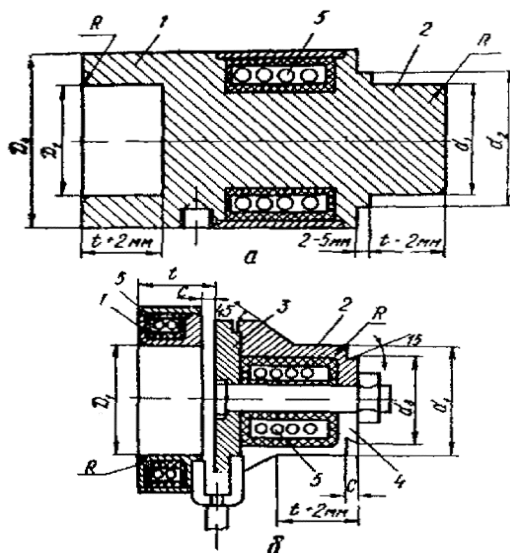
Инструмент для раструбной (а) и раструбно-стыковой (б) сварки:
